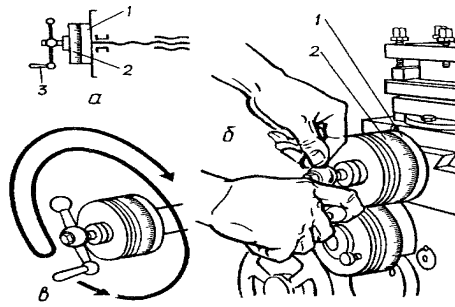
Лімб на гвинті поперечного супорта: а, б - лімб; в - схема користування лімбом; 1 - фланець на фартусі супорта; 2 - лімб; 3 - рукоятка гвинта поперечного супорта
